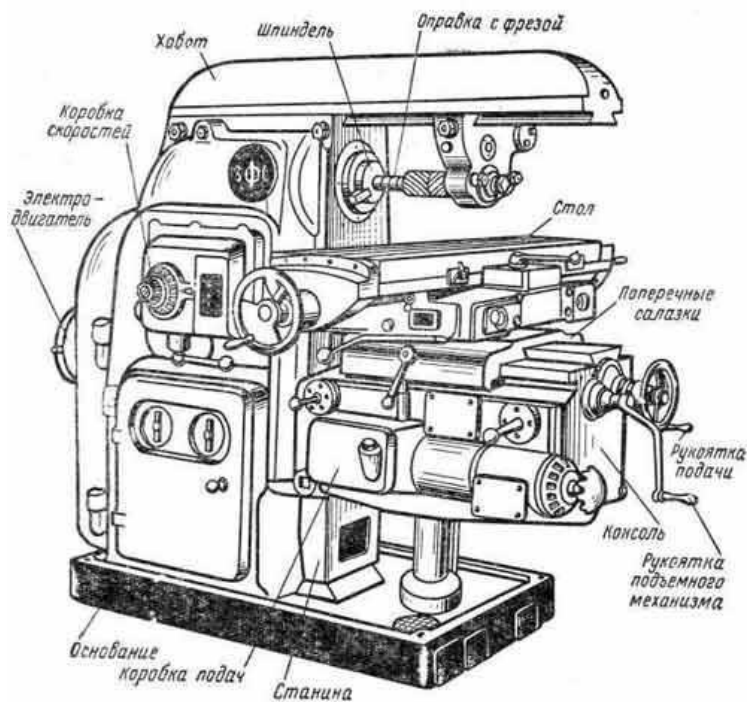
Основные части горизонтально-фрезерного станка 6Р83 (Горьковский завод фрезерных агрегатов)
